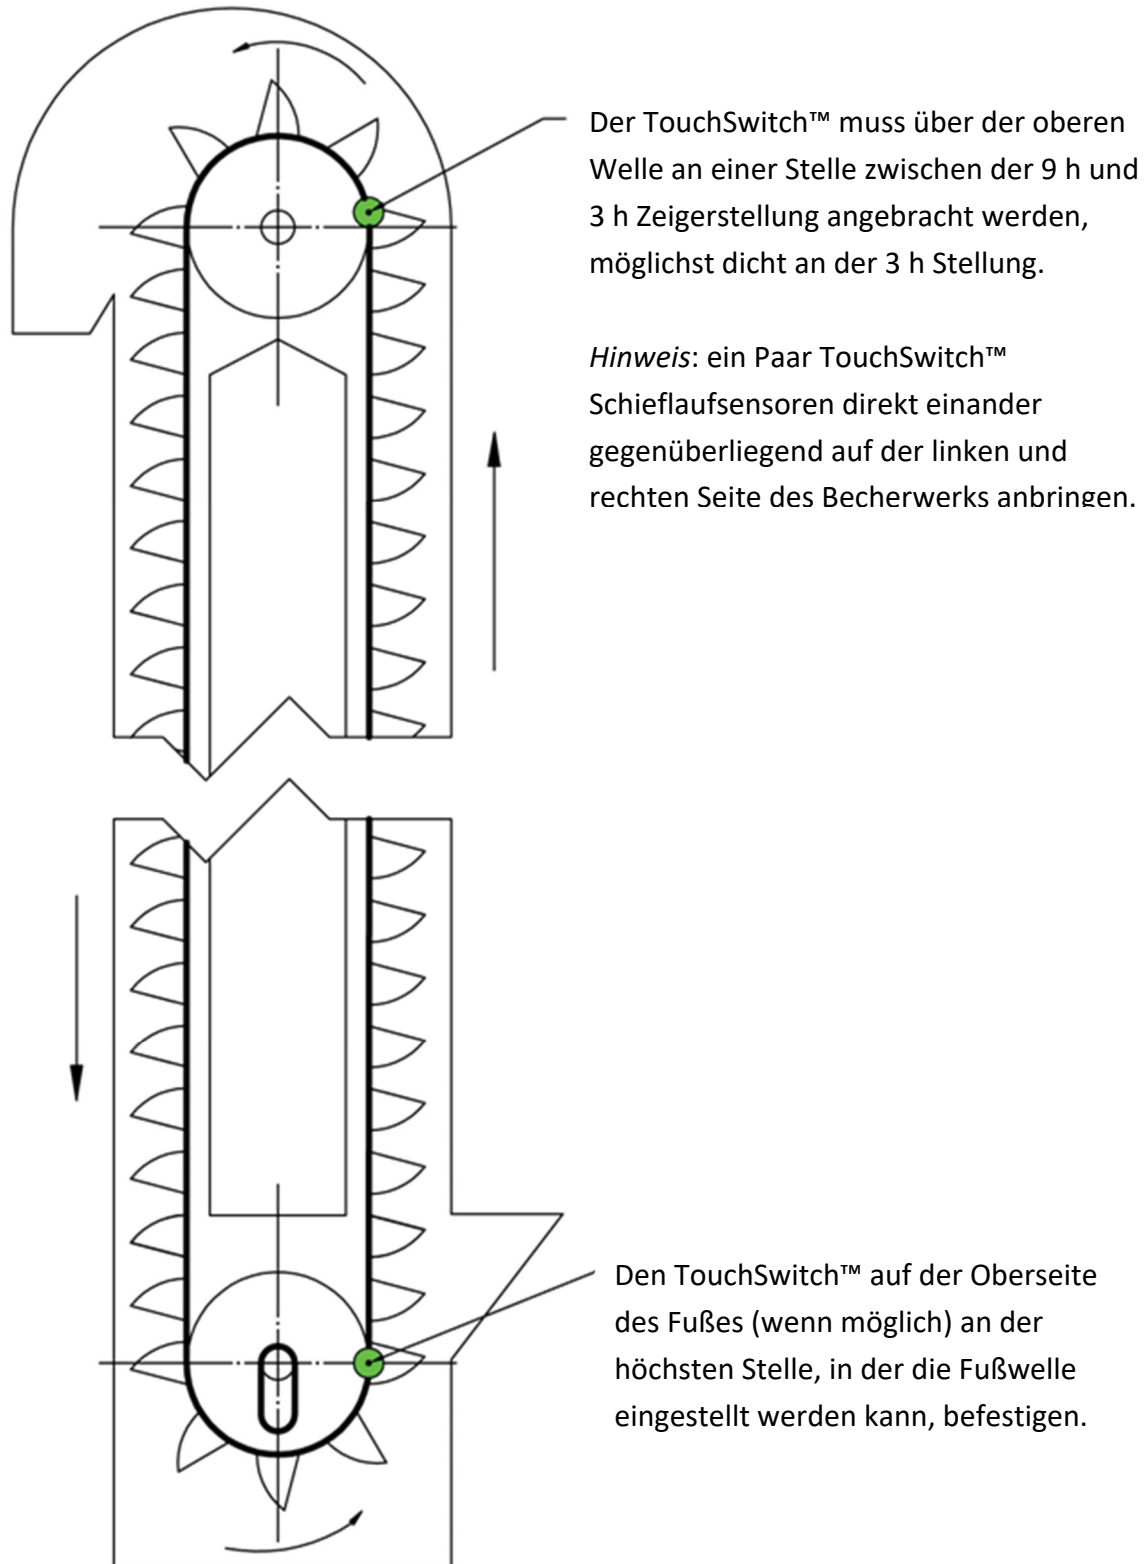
Montageposition TouchSwitch™ – Becherwerksfuß
